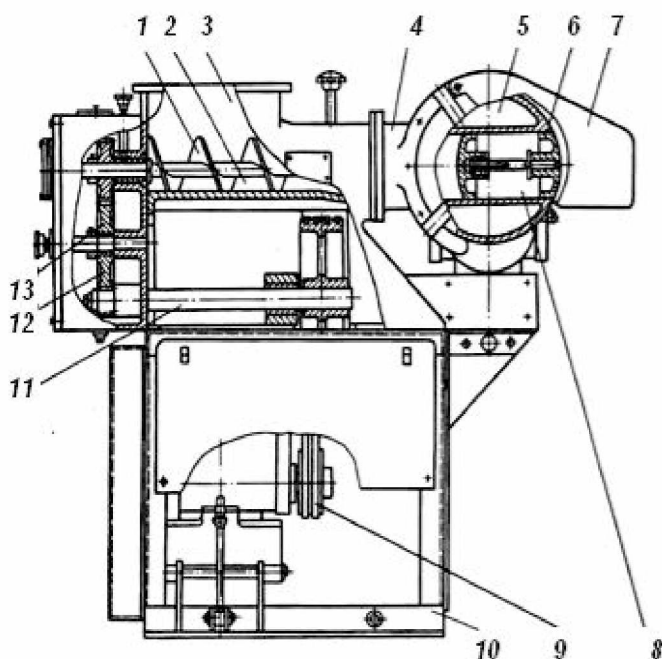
Тістоподільна машина ХДФ-М2: 1 - нагнітальні шнеки; 2 - робоча камера; 3 - приймальний бункер; 4 - горловина; 5 - подільна головка; 6 - поршень; 7 - захисний щиток; 8 - циліндрична проточка головки; 9 - клинопасова передача; 10 - станина; 11 - проміжний вал; 12, 13 - шестерні.
